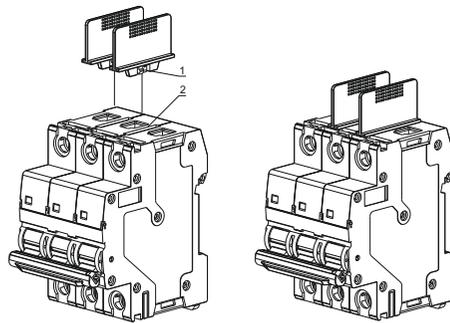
Монтаж перегородки / Figure 4 – Installation of the separating plate
